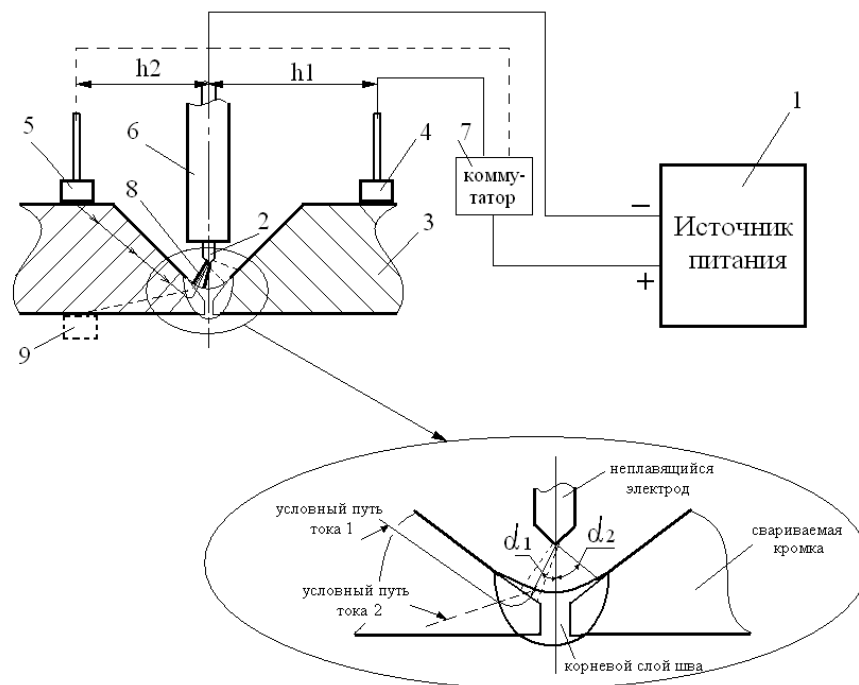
Схема процесса сварки дугой, отклоняемой собственным магнитным полем
